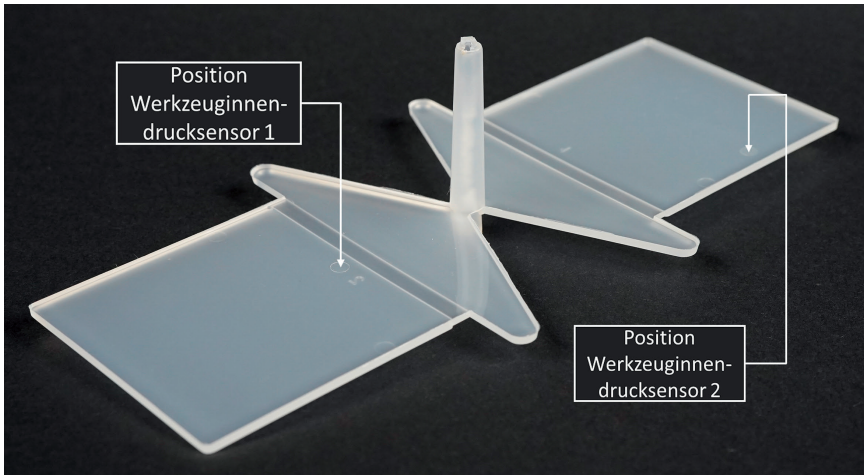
Das Werkzeug zur Formgebung des Platten-Formteils verfügt über zwei Werkzeuginnen-drucksensoren © IPE
